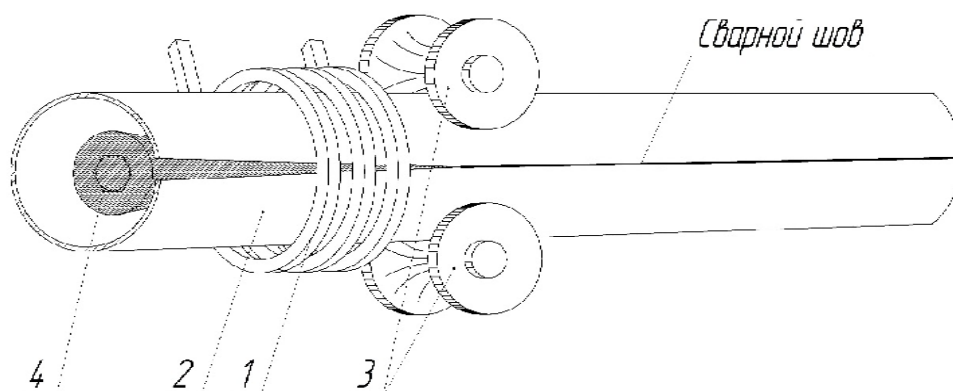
Схема высокочастотной сварки прямошовных труб:
